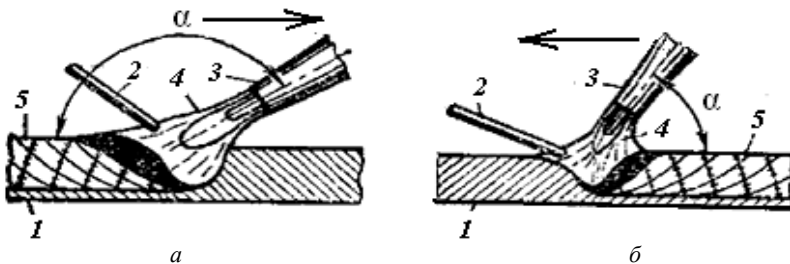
Способи зварювання: а - правий; б - лівий
